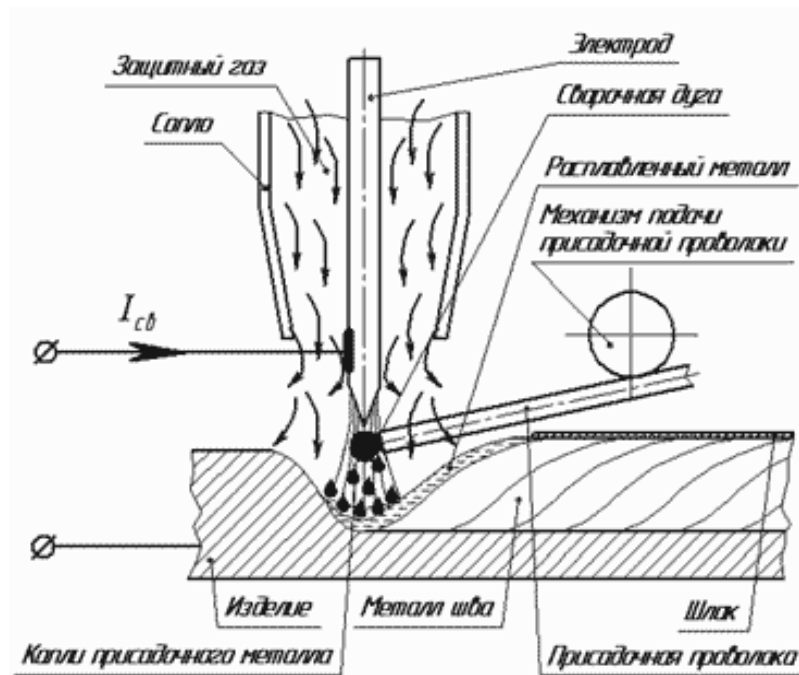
Схема сварки неплавящимся электродом с присадкой
